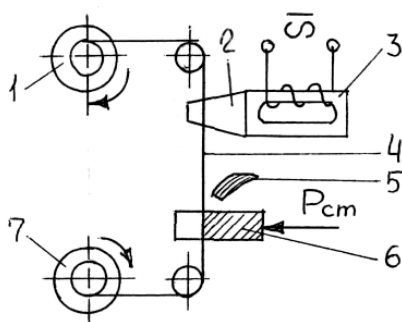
Схема розрізання непрофільованим інструментом – тонким дротом: 1,7 – котушки; 2 – концентратор; 3 – перетворювач; 4 – дріт-інструмент; 5 – сопло для подавання суспензії; 6 – заготовка
